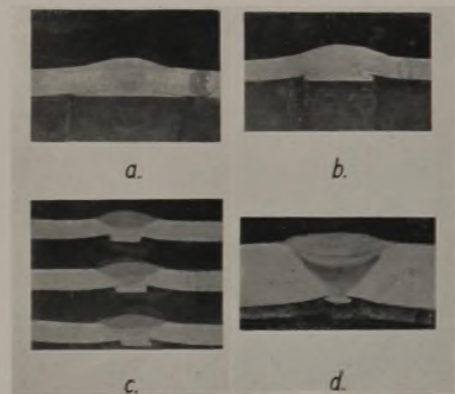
Autogene Rohrschweißungen mit verschiedenen Einlegerringformen
